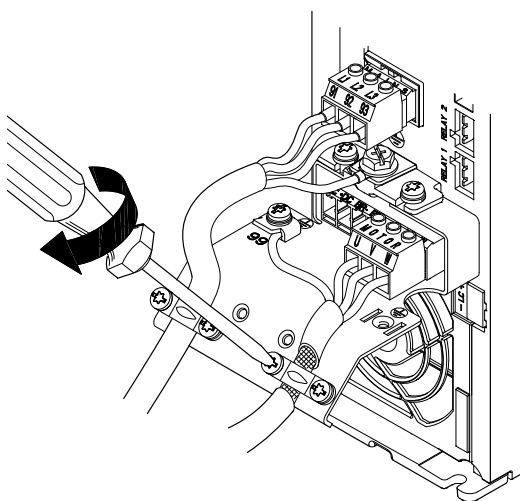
Branchement de la fiche moteur et fixation du câble blindé
